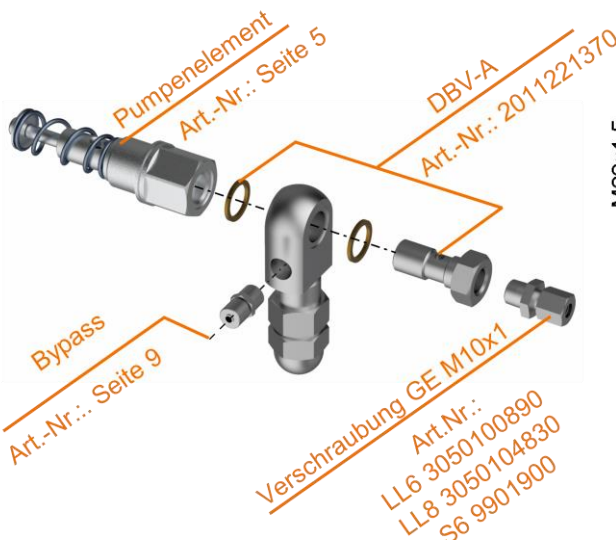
Explosionszeichnung PE mit DBV-A
